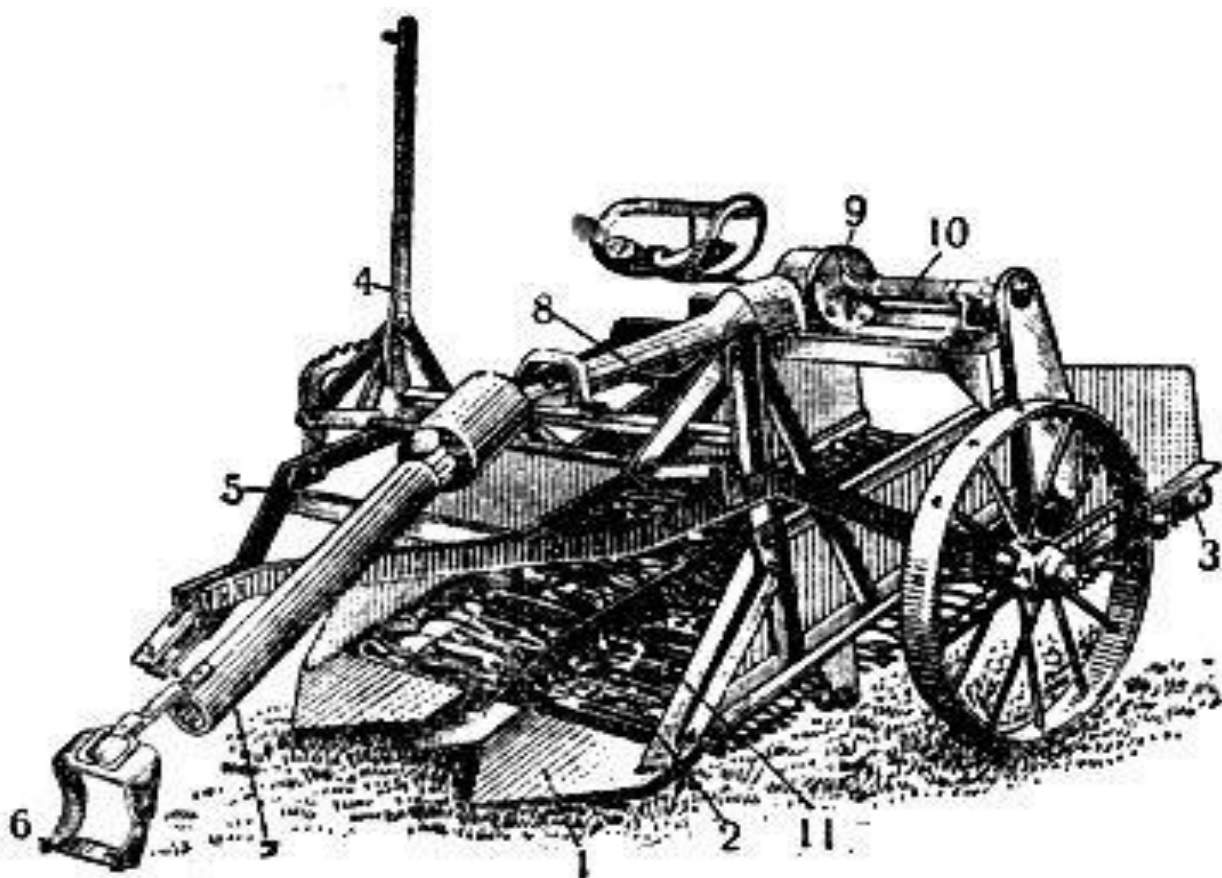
Однорядный элеваторный копатель «Джон Дир».
